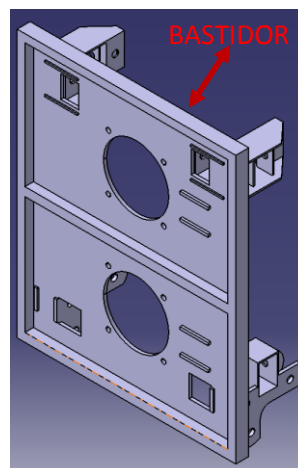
Conjunto soldado del grupo motor. Vista trasera 3D
